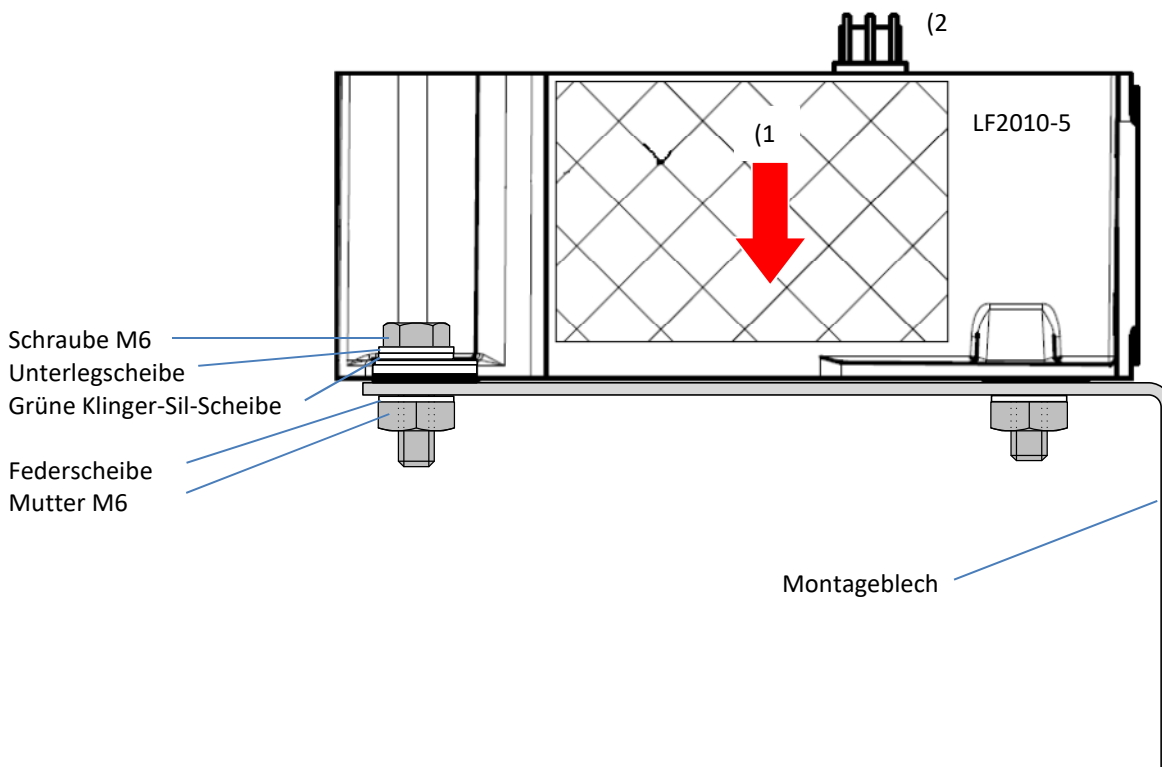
Seitenansicht des montierten Wandlers in Einbaulage,
